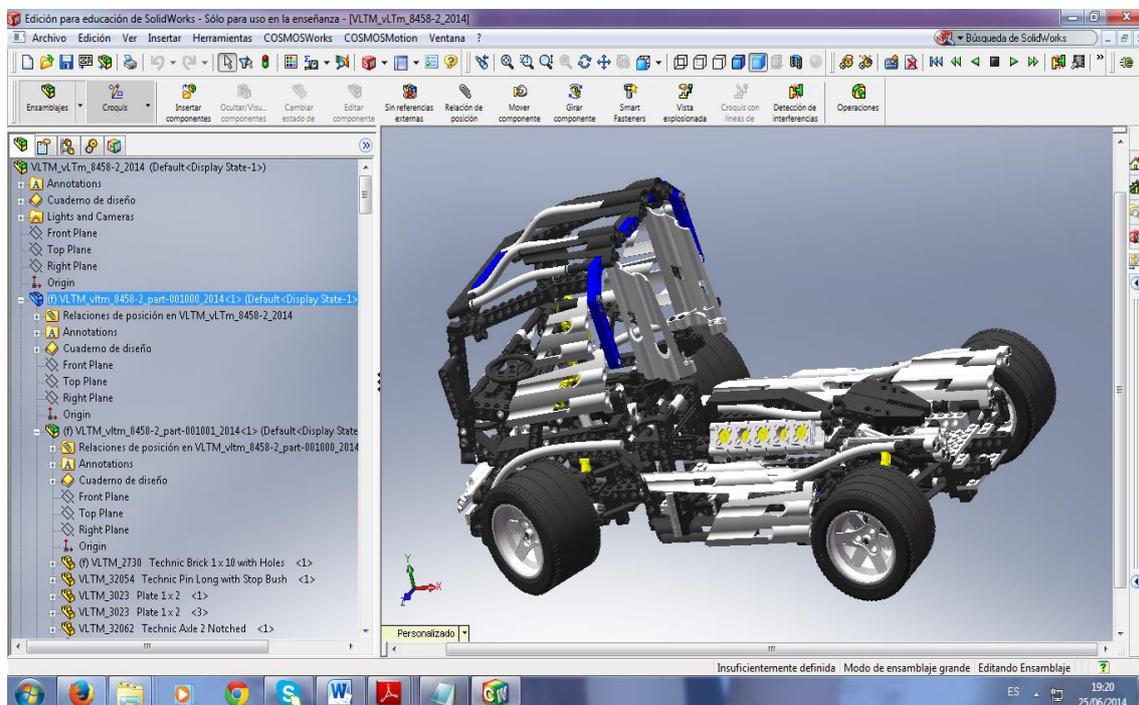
Entorno de trabajo de Ensamblajes en SolidWorks 2007.
